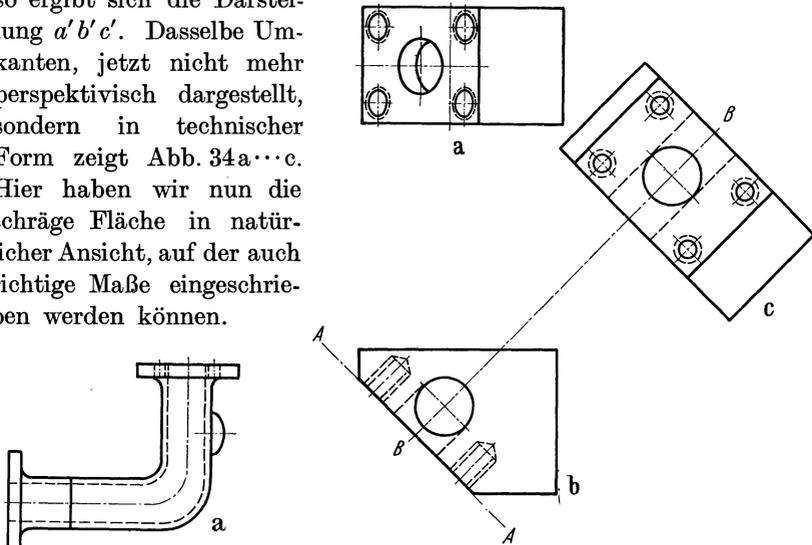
Schräge Klappung eines Blockes mit ebener und unverzerrter Ansicht der schrägen Fläche.
